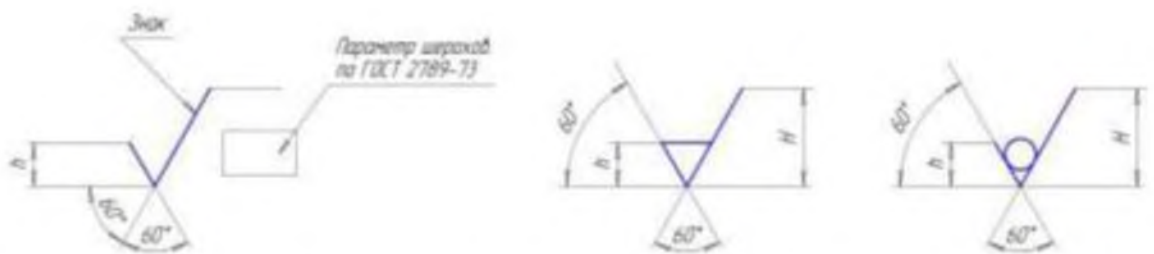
Обозначение шероховатости поверхностей: а) вид обработки конструктор не устанавливает; б) шероховатости поверхностей, получаемые удалением слоя материала; в) шероховатости поверхностей, которые получают без снятия слоя материала Пример выполнения.
